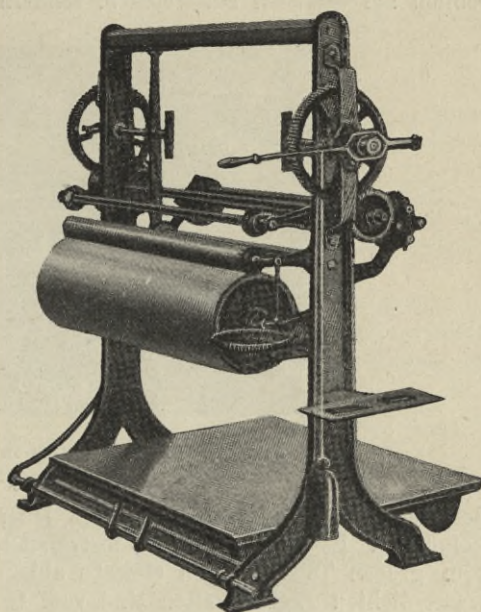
Maschine zum Aufziehen und Messen der Gewebe für die Automobilreifen.
